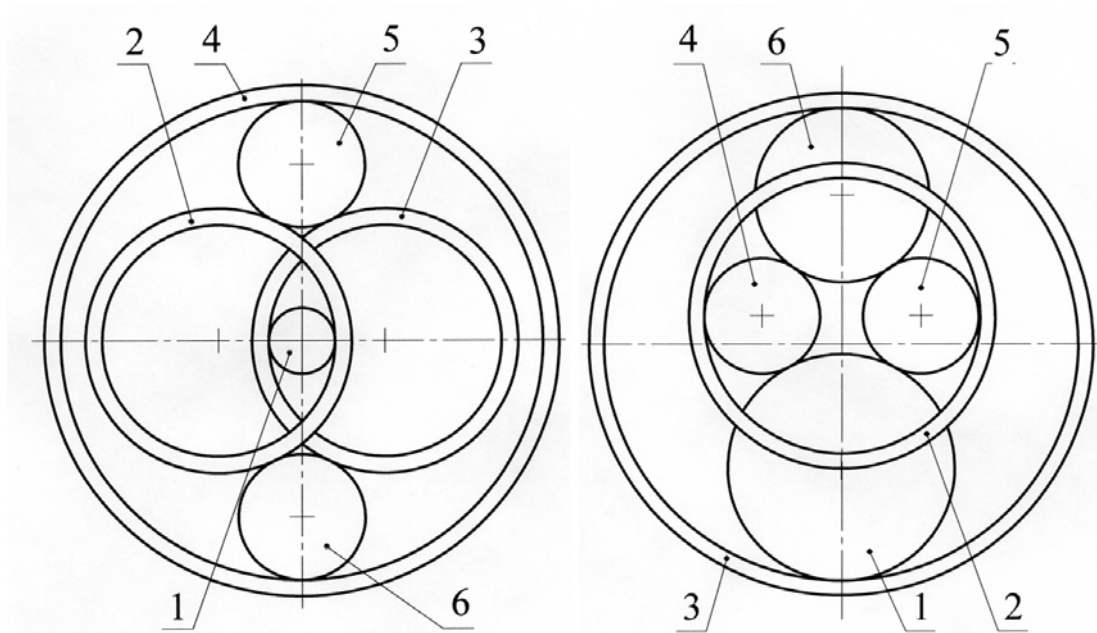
Бесепараторный подшипник (US4053191, E.W.Traut)
